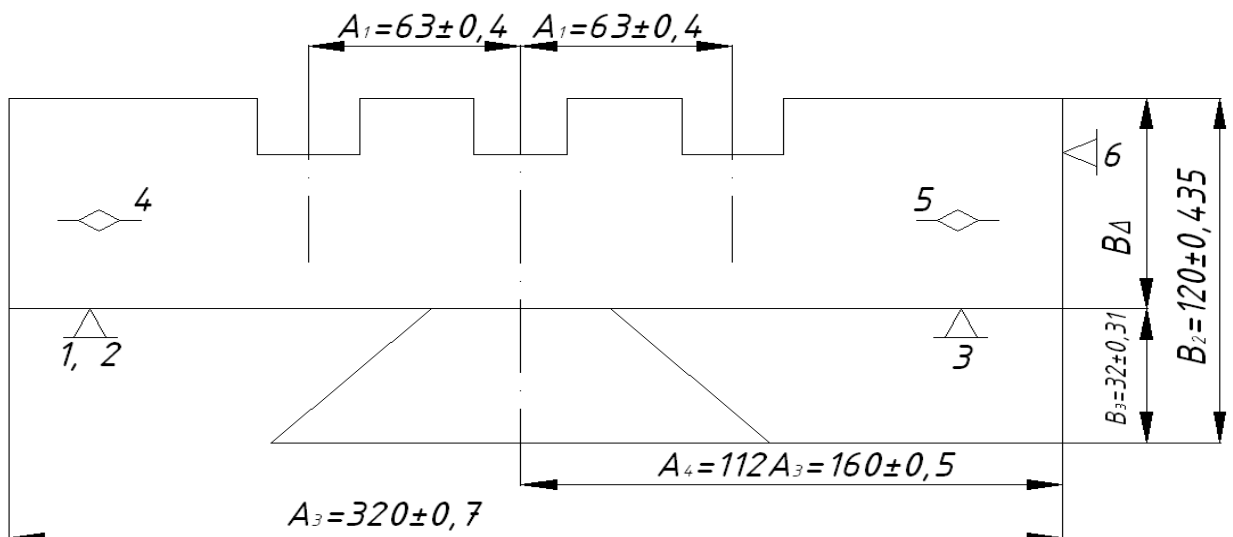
Теоретична схема базування при обробці Т-подібних пазів
